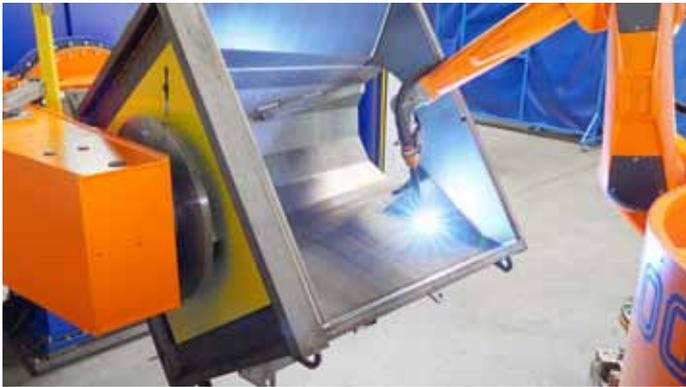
Der CLOOS-Schweißroboter erreicht mehr als 80 Prozent der Schweißnähte an dem komplexen Werkstück.
